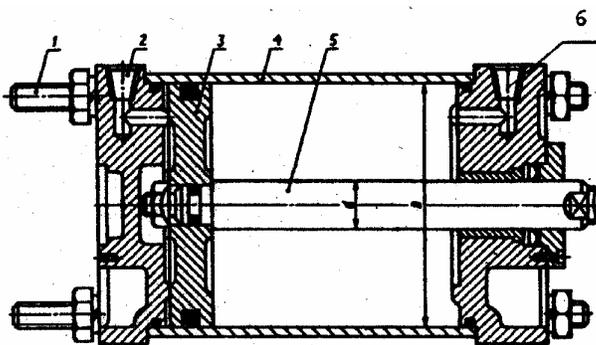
Стационарный пневмоцилиндр (1 – стяжки; 2 – задняя крышка; 3 – поршень; 4 – гильза; 5 – шток; 6 – передняя крышка)
